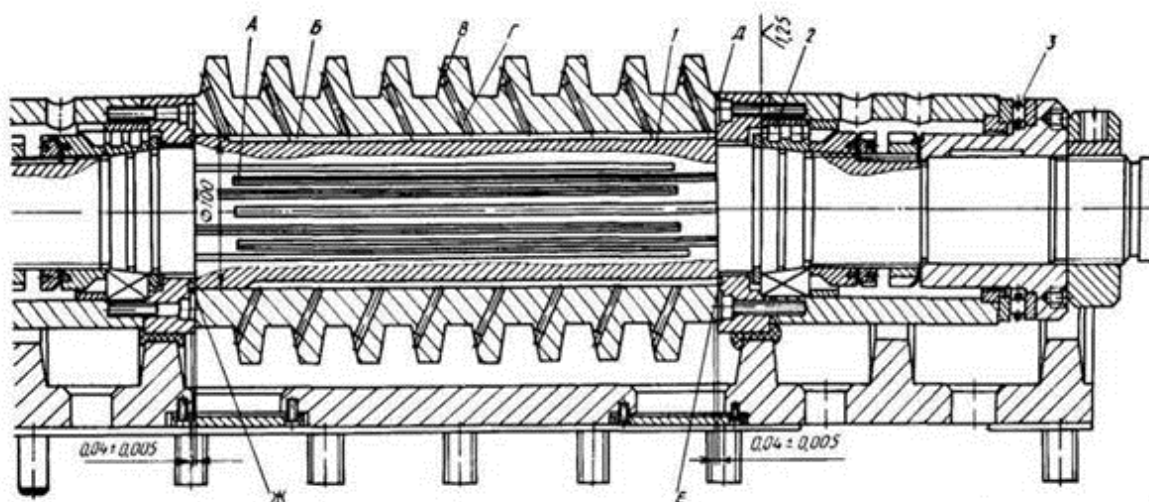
Конструкция червяка гидростатической червячно-реечной передачи
